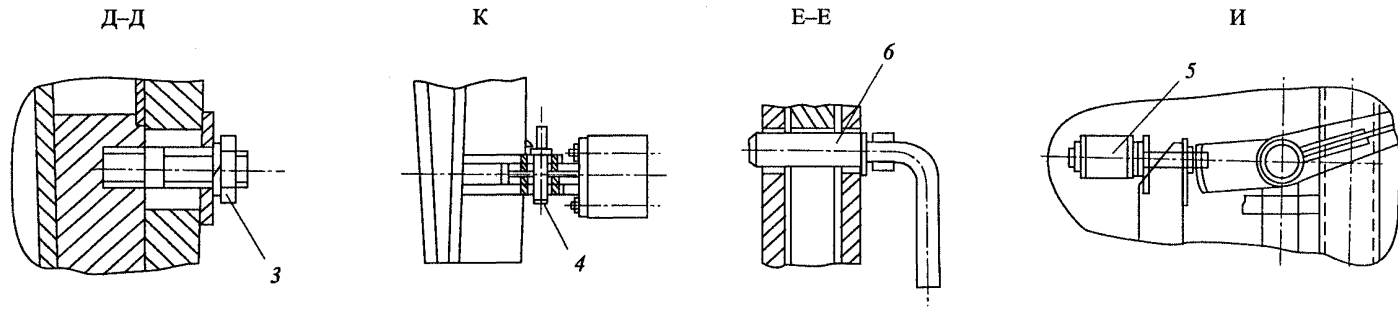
Схема приведения снегоочистителя фрезерно-роторного ФРЭС-2 в транспортное положение
